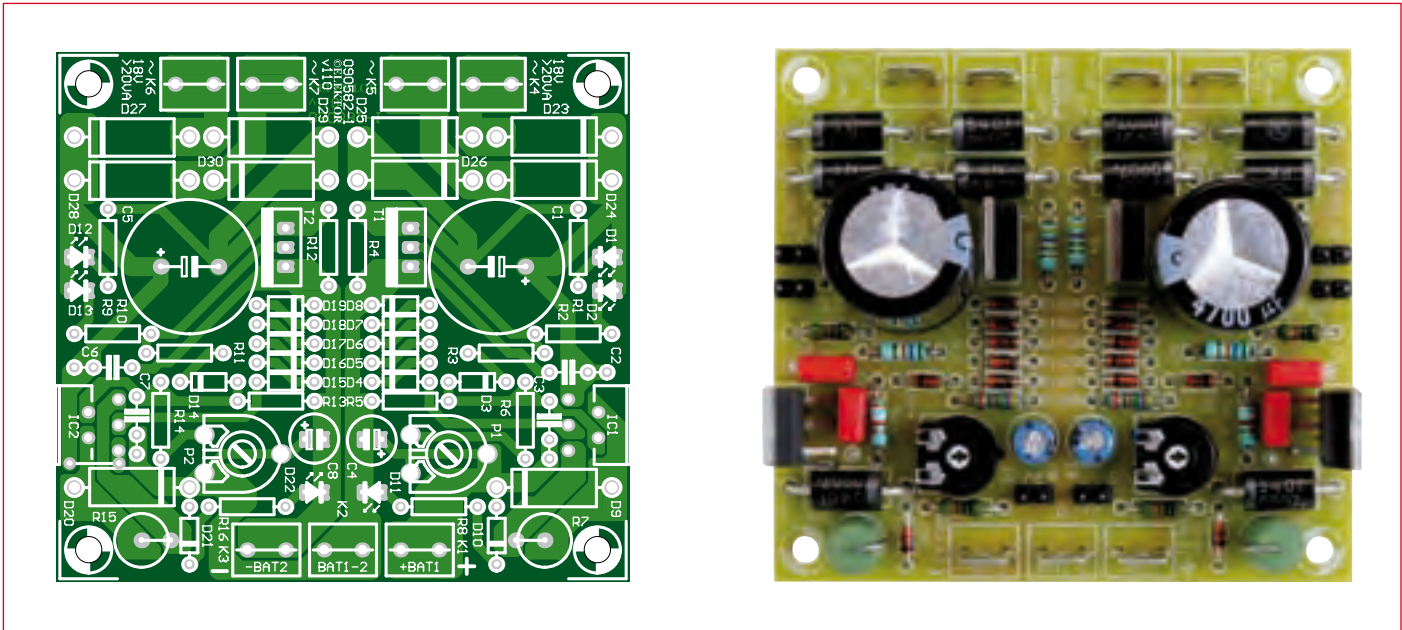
Hemos optado por componentes de montaje convencional para que la soldadura del circuito sea lo más sencilla posible.
